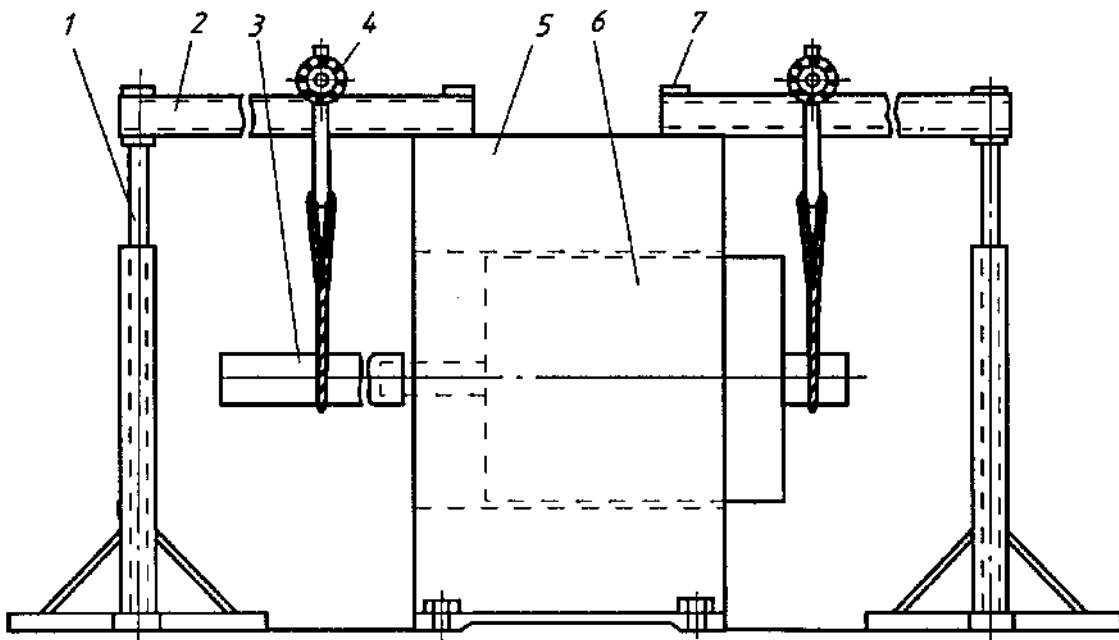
Приспособление для вывода ротора из статора: 1 – стойка; 2 – балка; 3 – удлинитель; 4 – грузовой ролик; 5 – статор; 6 – ротор; 7 – накладка – упор
